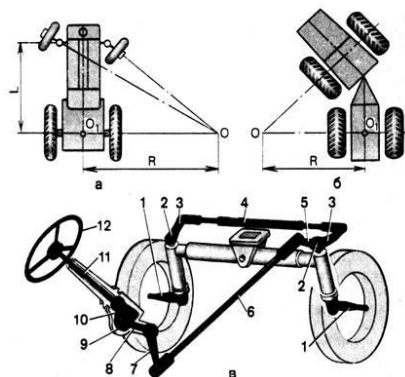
Схемы поворота и рулевое управление колесных тракторов: а – четырехколесного универсального трактора; б – трактора общего назначения с четырьмя ведущими колесами; в – рулевое управление; 1 – цапфы; 2 – шкворни; 3 – рулевые рычаги; 4 – поперечная тяга; 5 – поворотный рычаг; 6 – продольная тяга; 7 – рулевая сошка; 8 – вал рулевой сошки; 9 – сектор; 10 – червяк; 11 – рулевой вал; 12 – рулевое колесо
